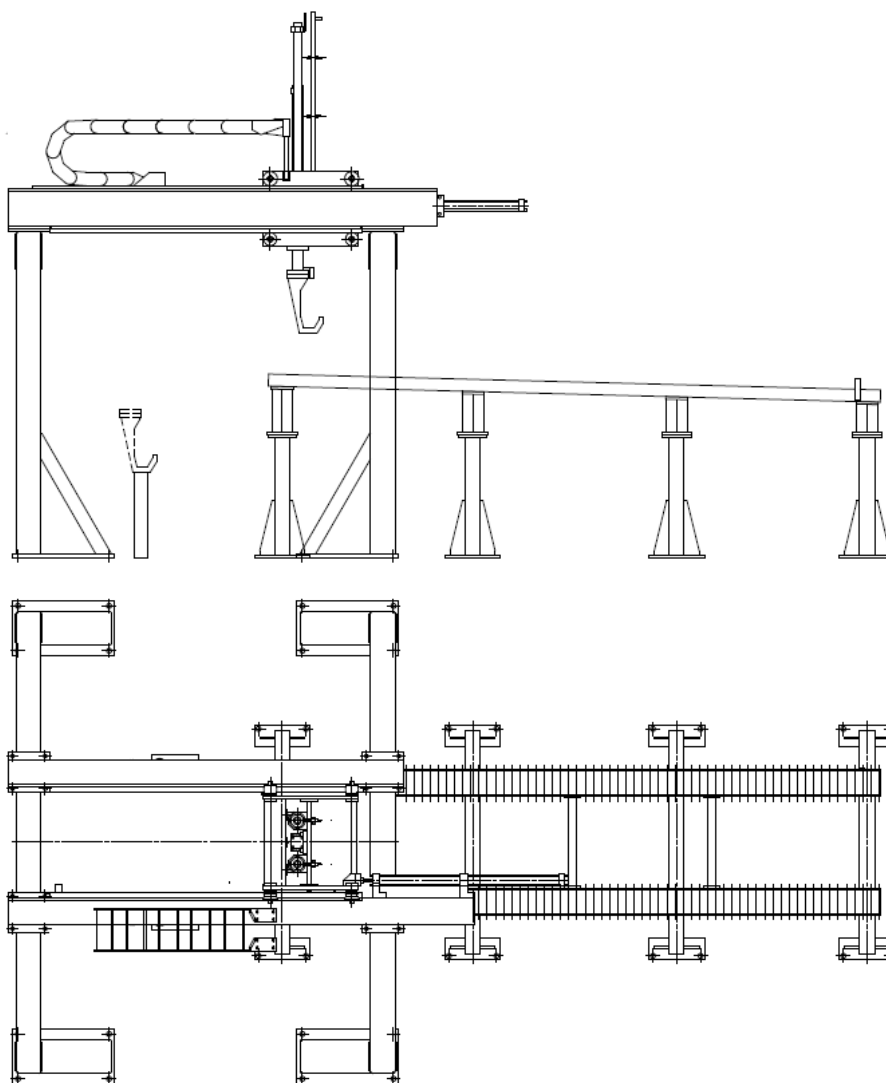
Сборочный чертеж конвейера до модернизации
